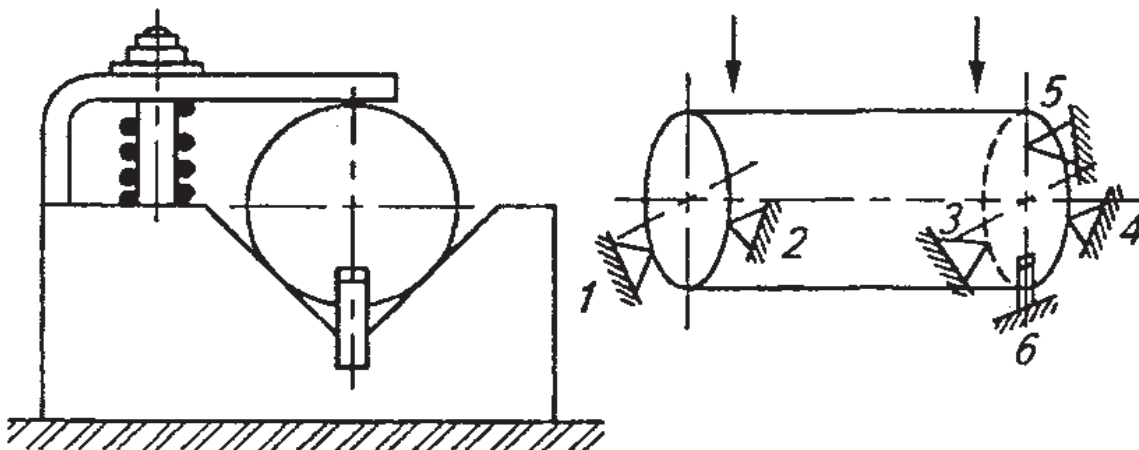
Схема базирования цилиндрической детали на призме: 1–6 – опорные точки
